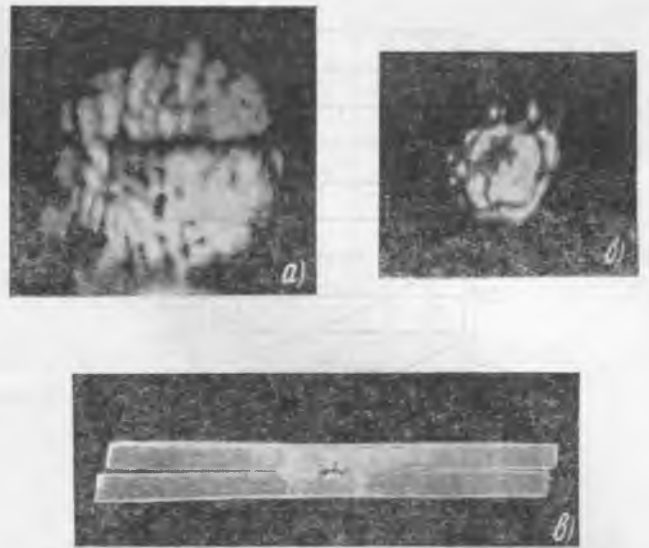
Изображения дефектов на экране с суспензией. а — неспровар в сварном шве; б — сварная точка; в — макроснимок с той же сварной точки.
